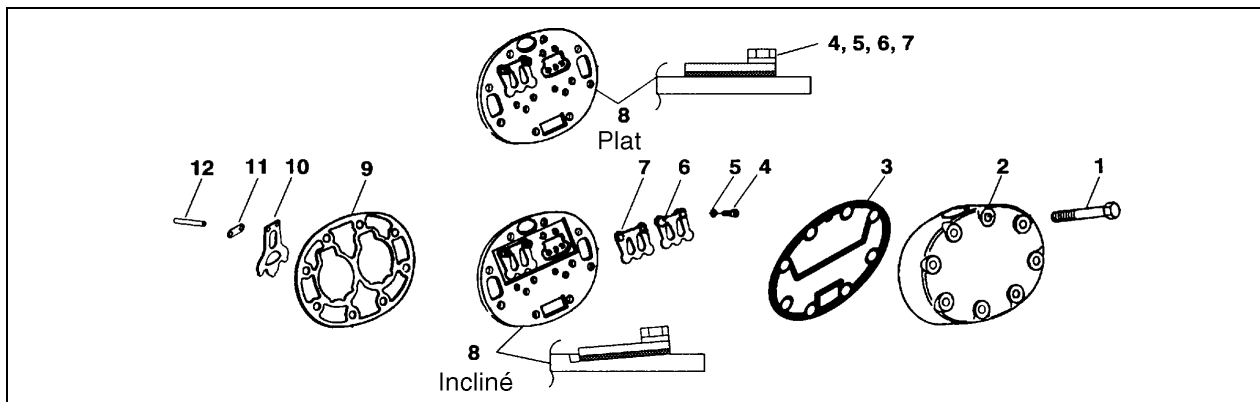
Pièces de culasse. (1) Vis d'assemblage; (2) Culasse; (3) Joint de culasse; (4) Vis d'assemblage; (5) Rondelle-frein; (6) Butée du clapet de refoulement; (7) Clapet de refoulement; (8) Plaque des clapets; (9) Joint de la plaque des clapets; (10) Clapet d'aspiration; (11) Ressort de positionnement; (12) Cheville.
